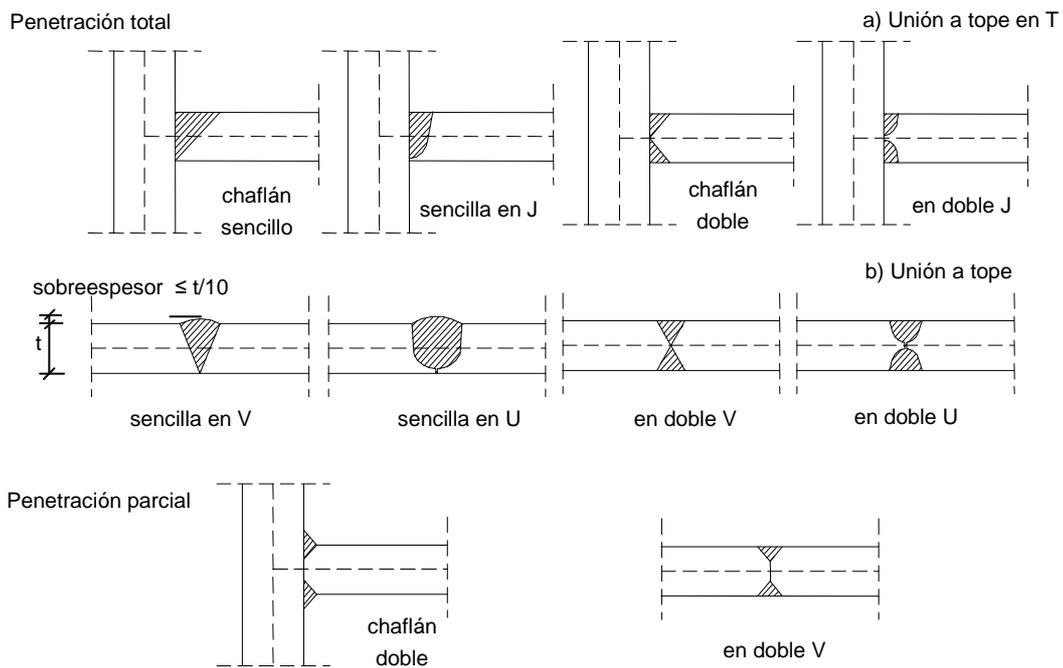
Soldadura a tope y formas de preparación
